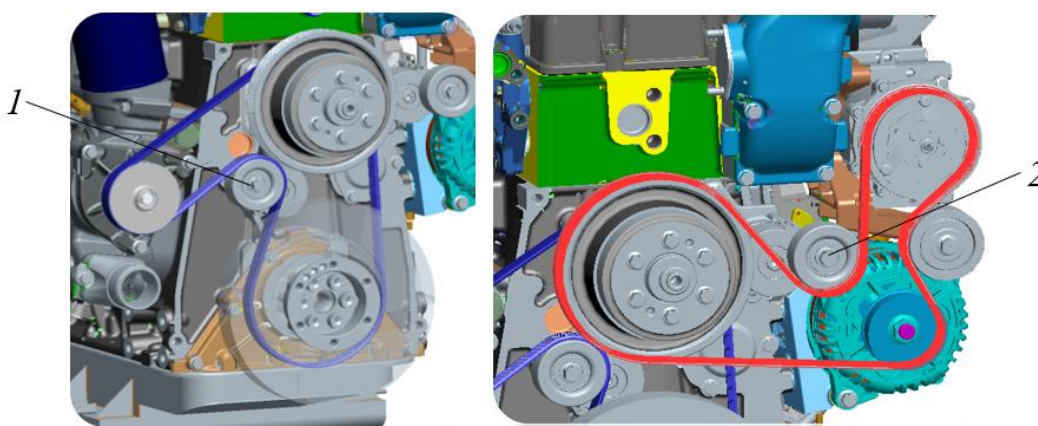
Ременный привод агрегатов двигателя ЯМЗ-534
